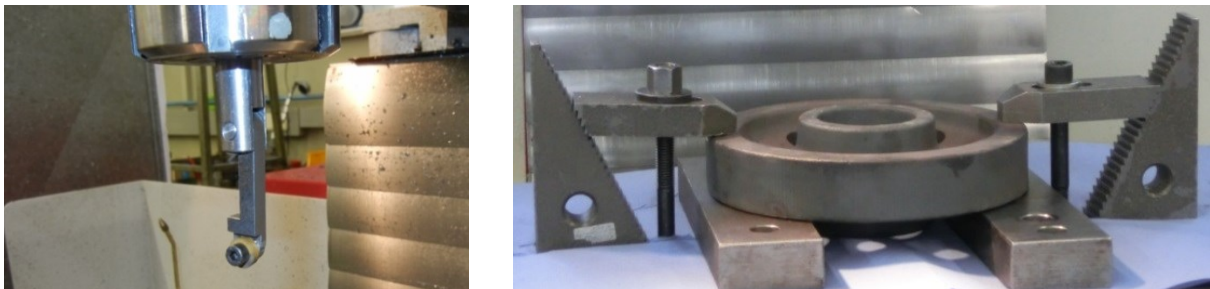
Eingespanntes Werkzeug in der Maschinenspindel (links) und aufgespannter Versuchsträger auf dem Maschinentisch (rechts)
